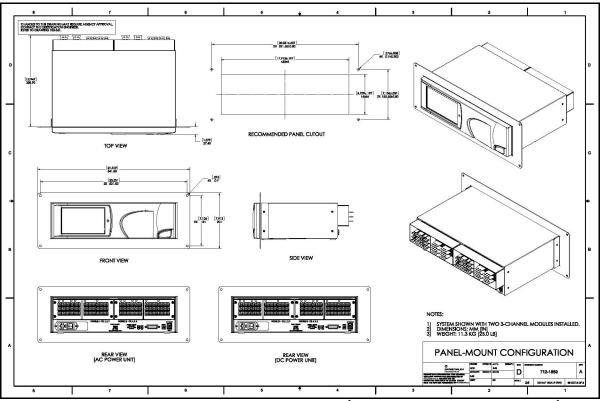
Configuração de montagem em painel (desenho 712-1889\_revA, SH 3 de 3)
